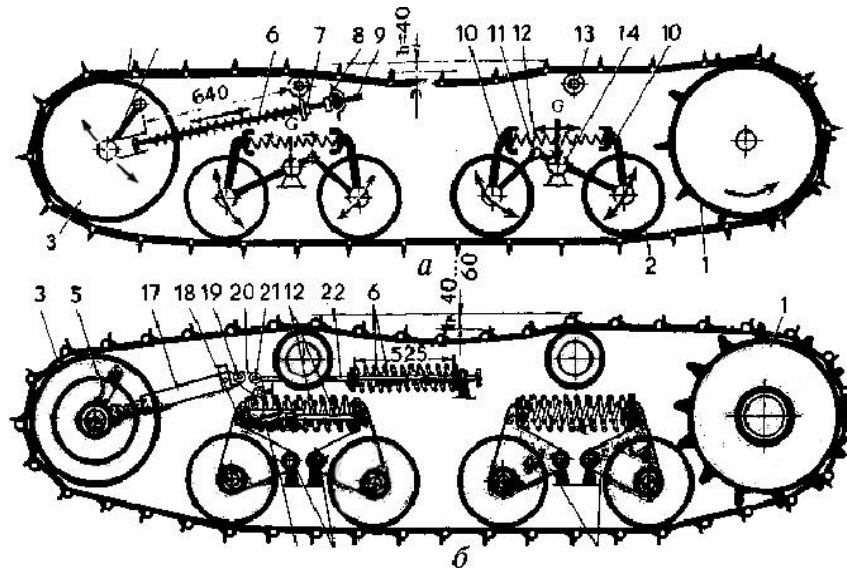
Схема гусеничних рушіїв машини 1 - привідна зірочка; 2 - опорний каток; 3 - напрямне колесо; 4 - гусеничний ланцюг; 5 - колінчаста вісь; 6 – пружина амортизуюча; 7 - гайка пружини; 8 – натяжна гайка гвинта; 9 - натяжний гвинт; 10 - балансири каретки; 11 - шарнір балансирів; 12 - пружини каретки; 13 - підтримуючий ролик; 14 - цапфа каретки; 15 - цапфи балансирів; 16 - гідроамортизатори; 17 - циліндр гідронатяжителя; 18 - палець гідроамортизатора; 19 - палець головки гідроциліндра; 20 - проміжна ланка; 21 - палець натяжного болта; 22 - натяжний болт
